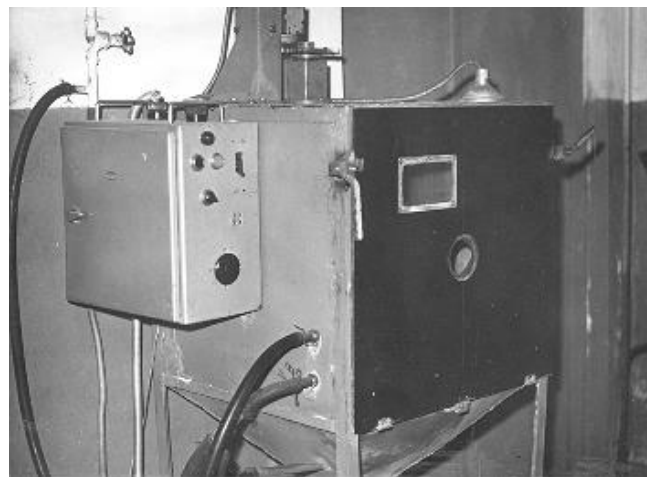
Дробоструменева установка для обробки оправок з поршневыми кільцями перед напилюванням
